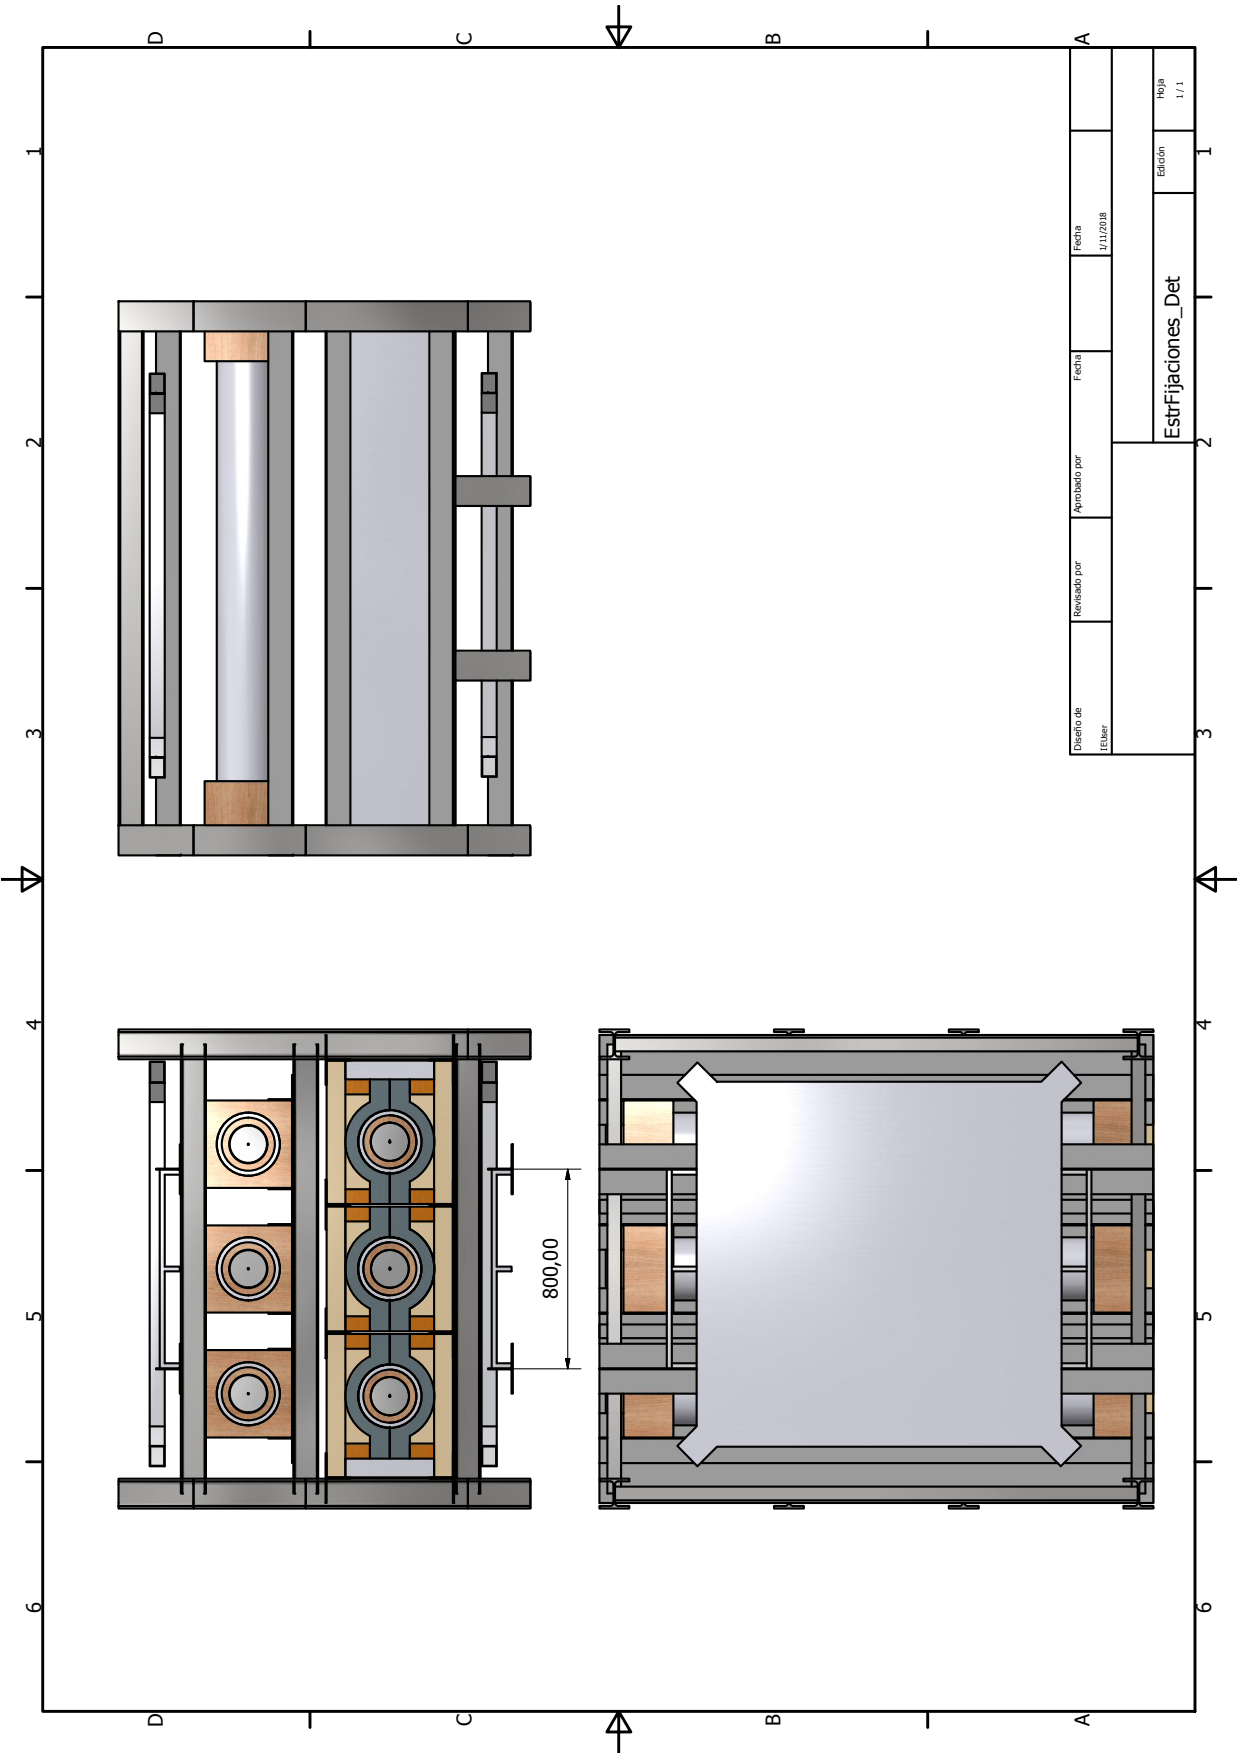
Estructura de soporte con los detectores fijados (mm).
